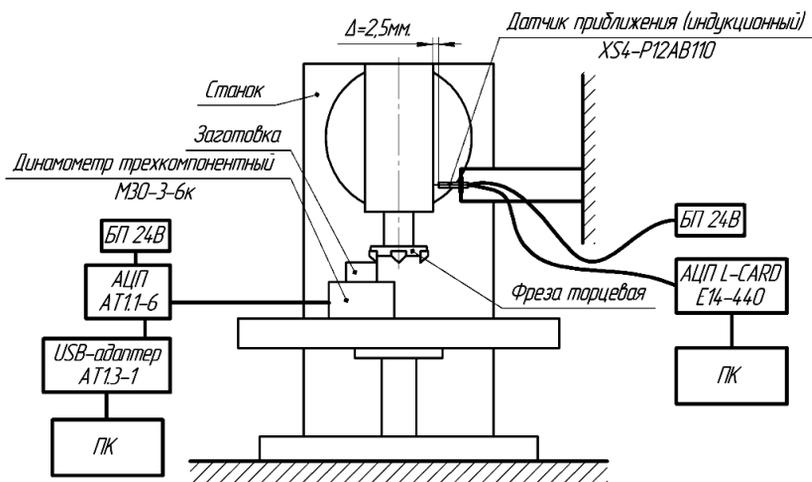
Схема измерения сил резания и колебаний станка при торцевом фрезеровании
